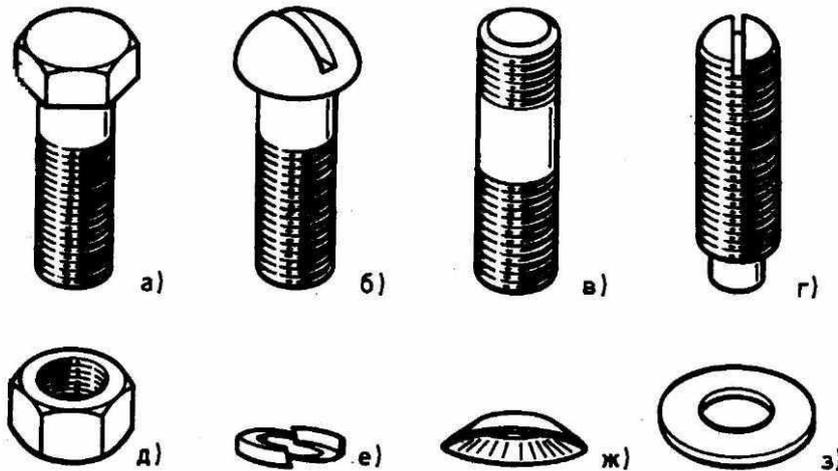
Конструктивные элементы резьбовых соединений: а — болт; б — винт; в — шпилька; г — установочный винт; д — гайка; е — пружинная шайба; ж — деформируемая шайба; з — плоская шайба
